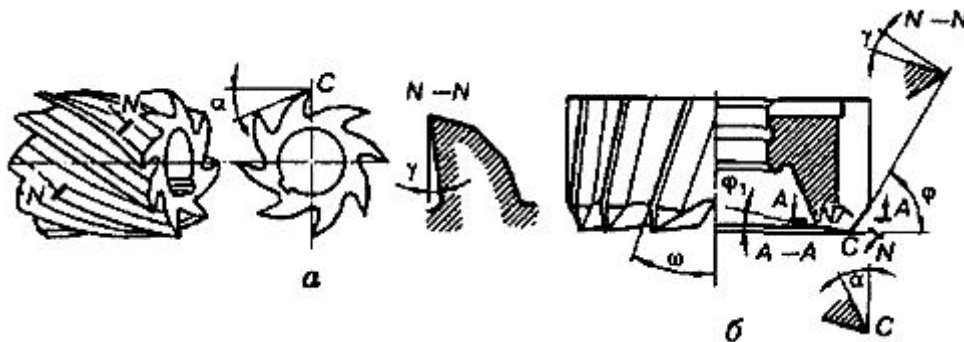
Основні геометричні параметри циліндричної і торцевої фрез
